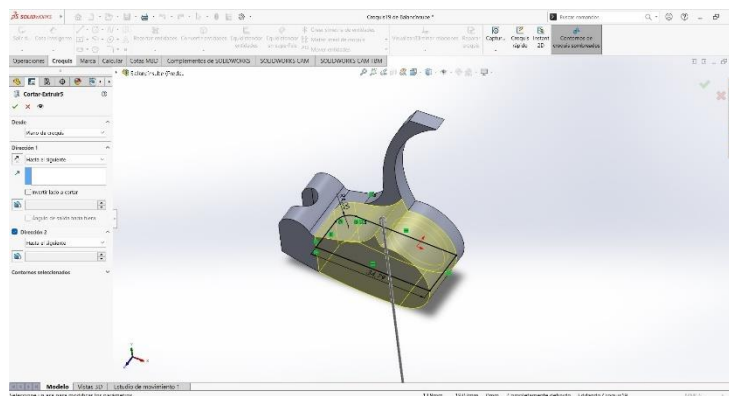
Balancín 1 (Extrusionado de corte de Croquis 6). Fuente: SolidWorks
